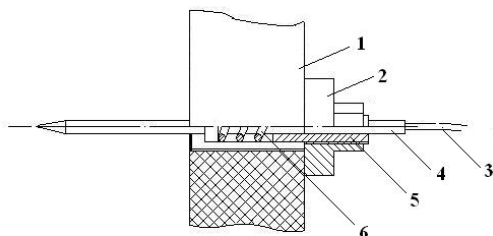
Конструкция *одноконтактного измерительного устройства*: 1 – стенка; 2 – корпус; 3 – провод; 4 – измерительный контакт; 5 – втулка; 6 – упругий элемент
